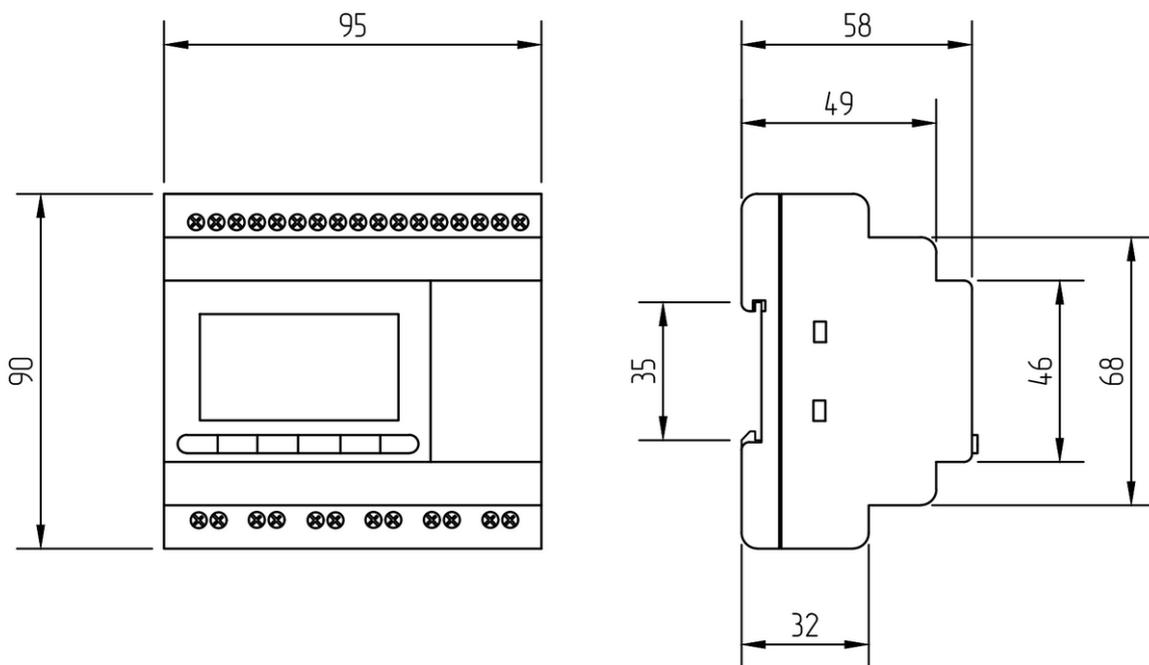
Габаритные и установочные размеры модуля ЦПУ
